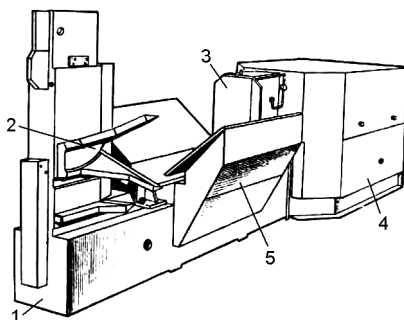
Схема окорочного станка для круглых лесоматериалов
